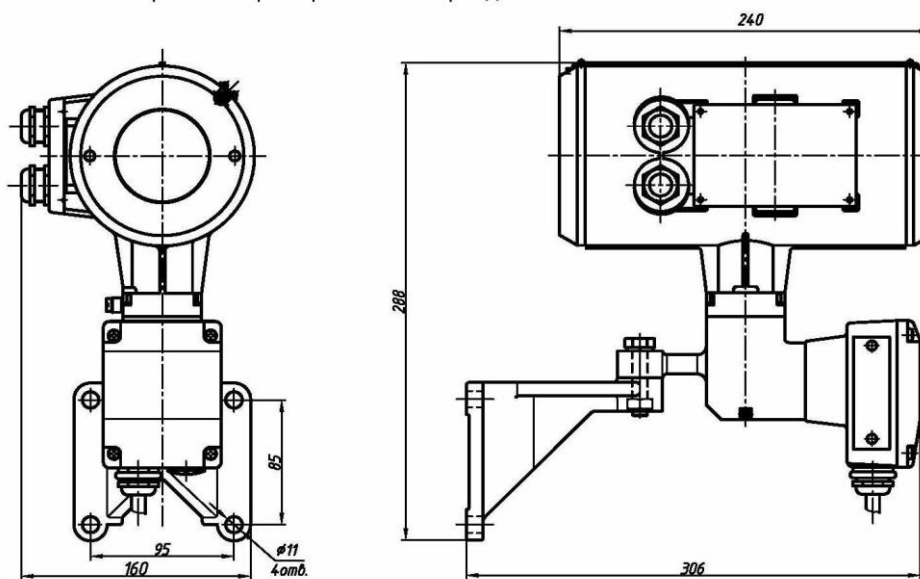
Габаритные размеры сигнального конвертера (СК)
